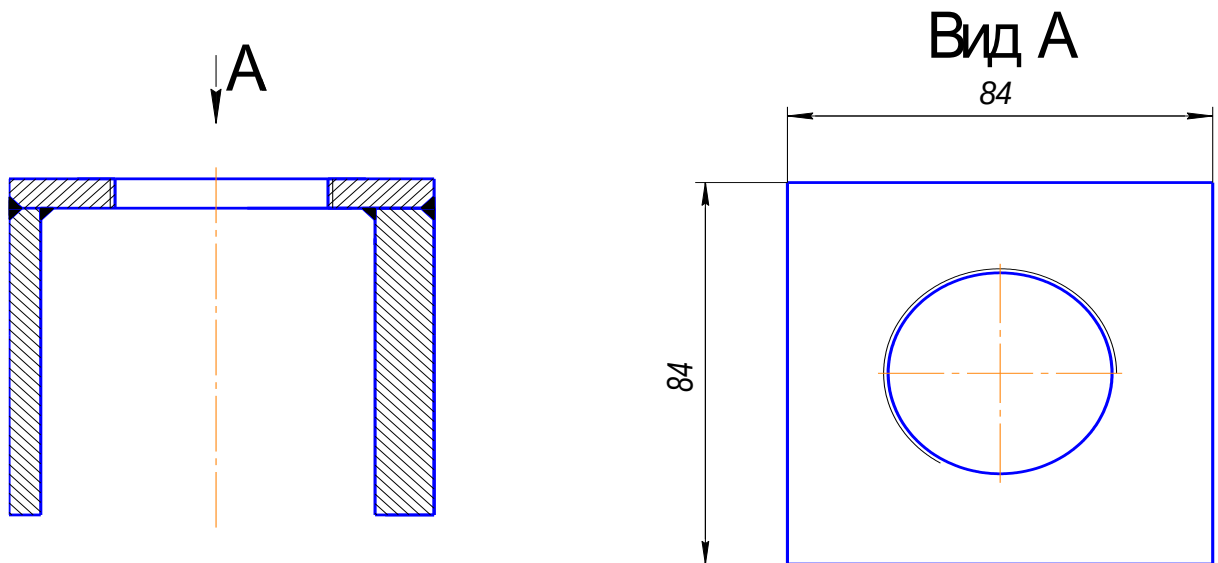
Схема зварного з'єднання корпусу мотор-редуктора
